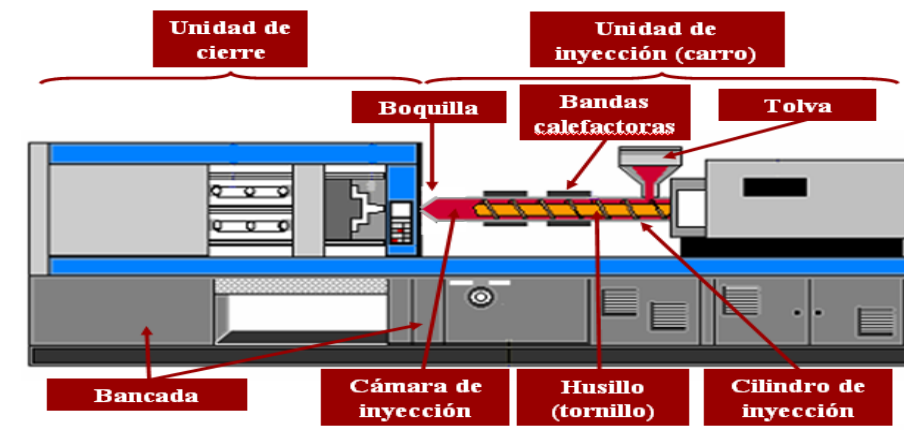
Partes de una inyectora<sup>3,5</sup>
